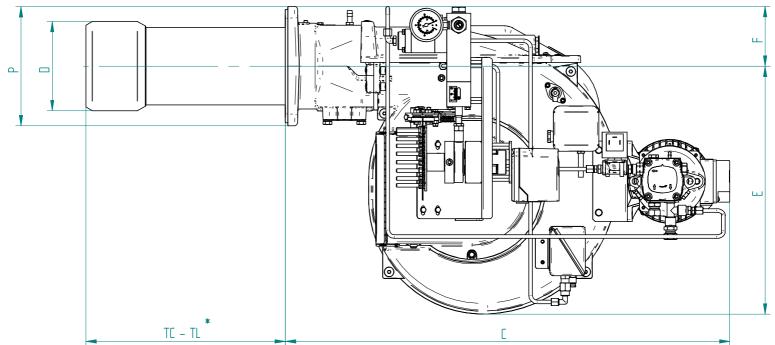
Dimensioni ingombro FGP 50/M EVO
